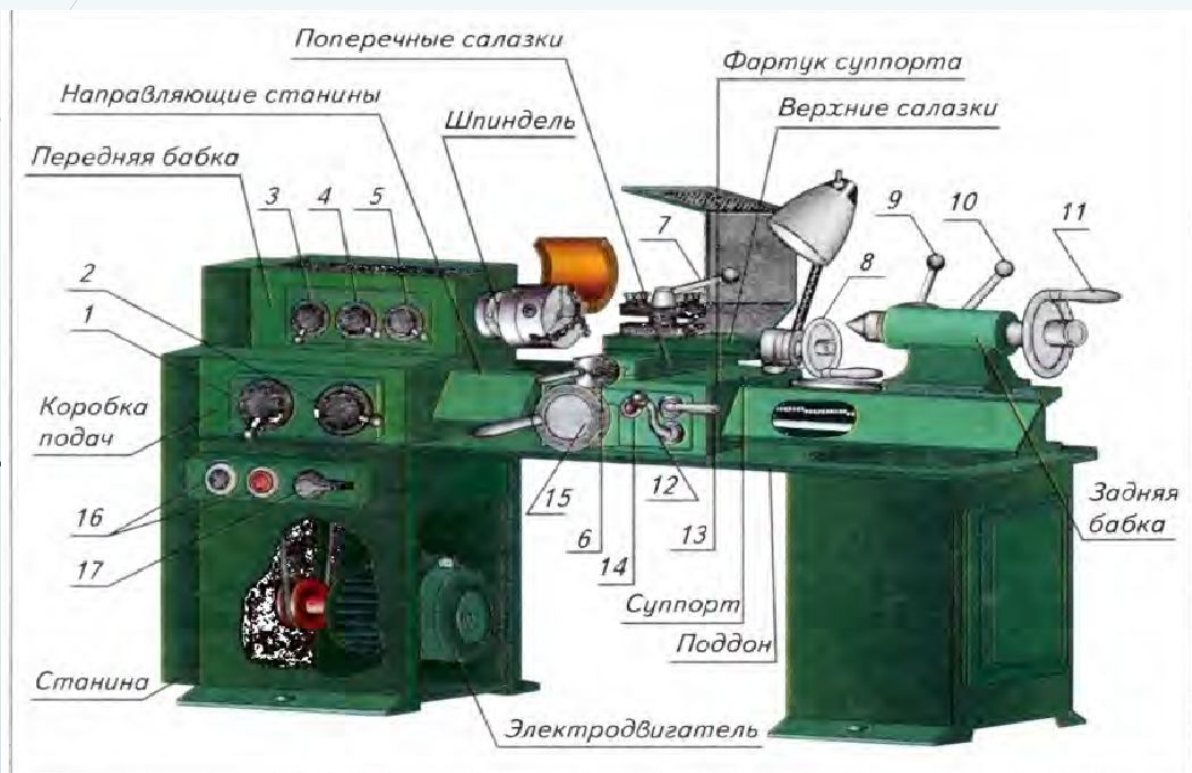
Токарно-винторезный станок ТВ-6: 1, 2 — рукоятки переключения величины подачи; 3 — рукоятка переключения гитарного механизма; 4, 5 — рукоятки переключения частоты вращения шпинделя; 6 — рукоятка поперечной подачи суппорта; 7 — рукоятка закрепления резцедержателя; 8 — рукоятка перемещения верхних салазок; 9 — рукоятка крепления пиноли; 10 — рукоятка крепления задней бабки; 11 — маховик подачи пиноли; 12, 13 — рукоятки управления механической подачей; 14 — кнопка включения реечной передачи; 15 — маховик перемещения суппорта; 16 — кнопки включения и отключения электродвигателя; 17 — рукоятка реверса
